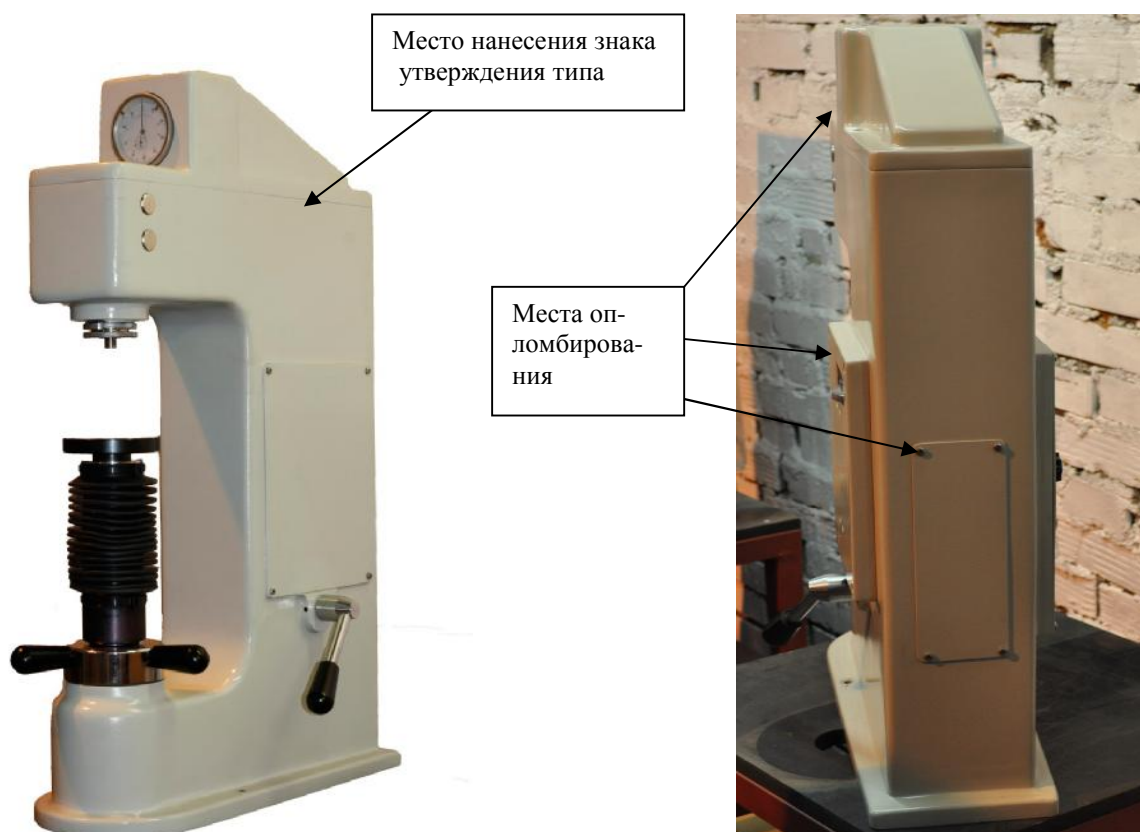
Внешний вид твердомеров, места расположения пломб и знака утверждения типа.
